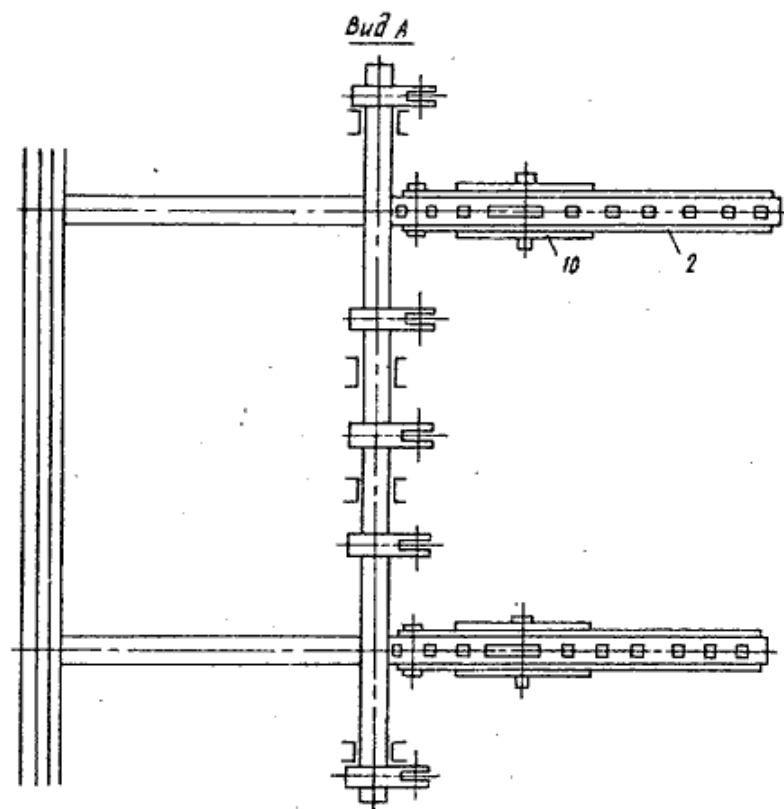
Приводное устройство штангового толкателя, вид А
